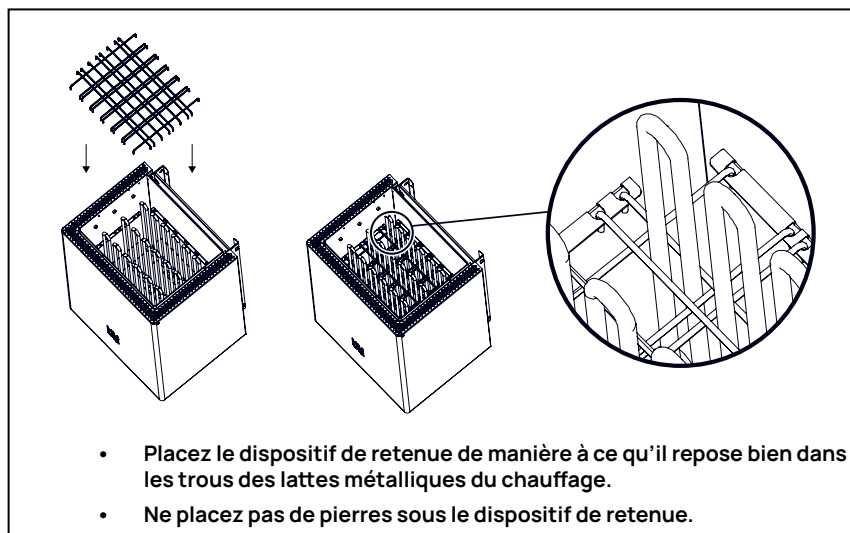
Installation du dispositif de retenue du HUUM CORE Wall et CORE Wall Combi.
